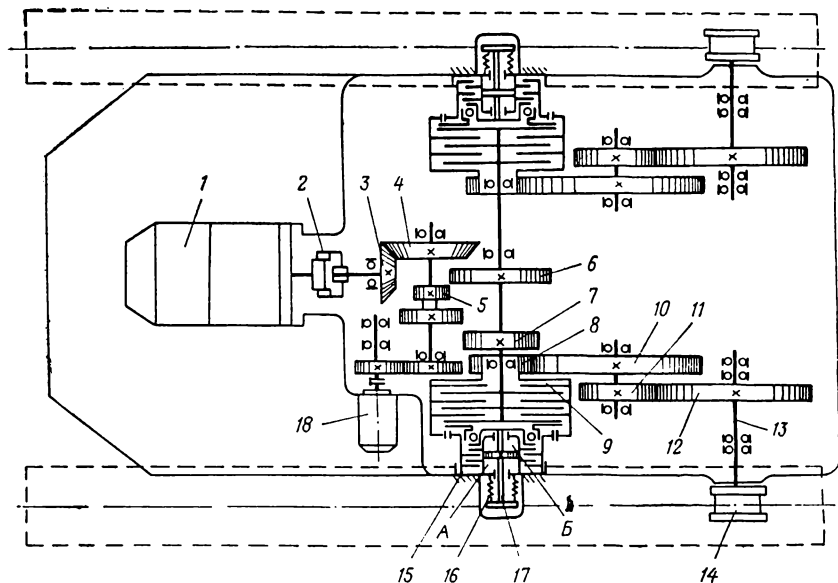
Кинематическая схема гусеничной ходовой части погрузочной машины 1ПНБ-2 с центральным расположением двигателя
